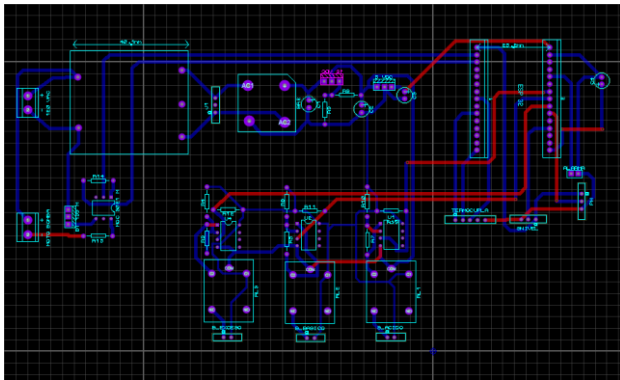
, Primer Diseño en Proteus de la PCB del Prototipo.
